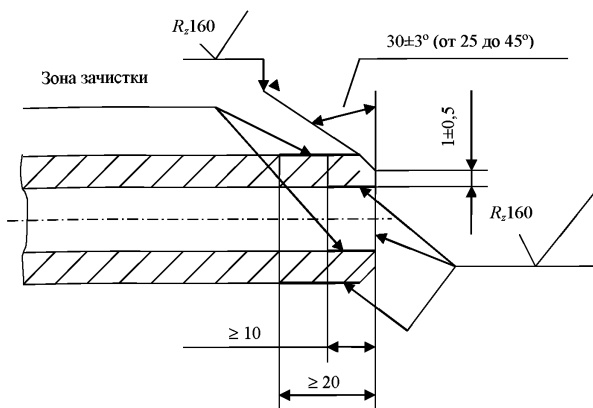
Обработка и зачистка кромок труб под сварку
